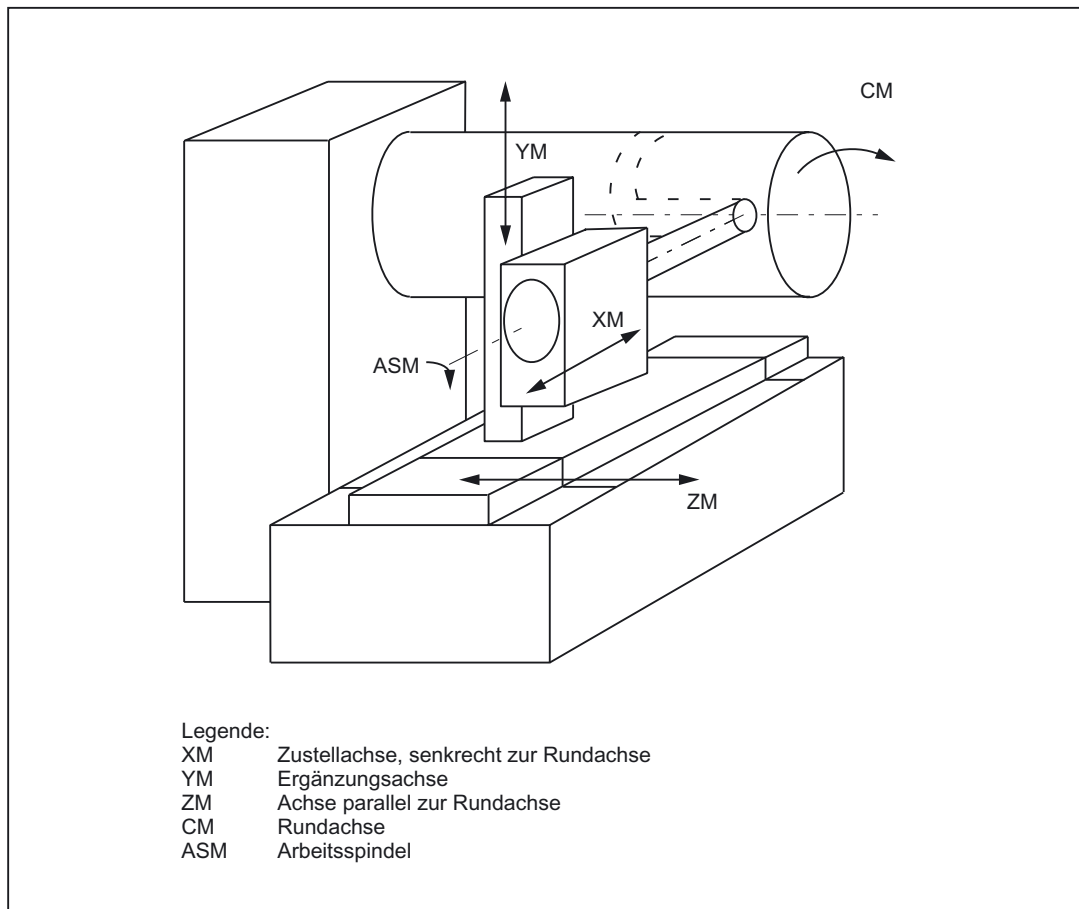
Nutbearbeitung am Zylindermantel mit X-Y-Z-C-Kinematik
